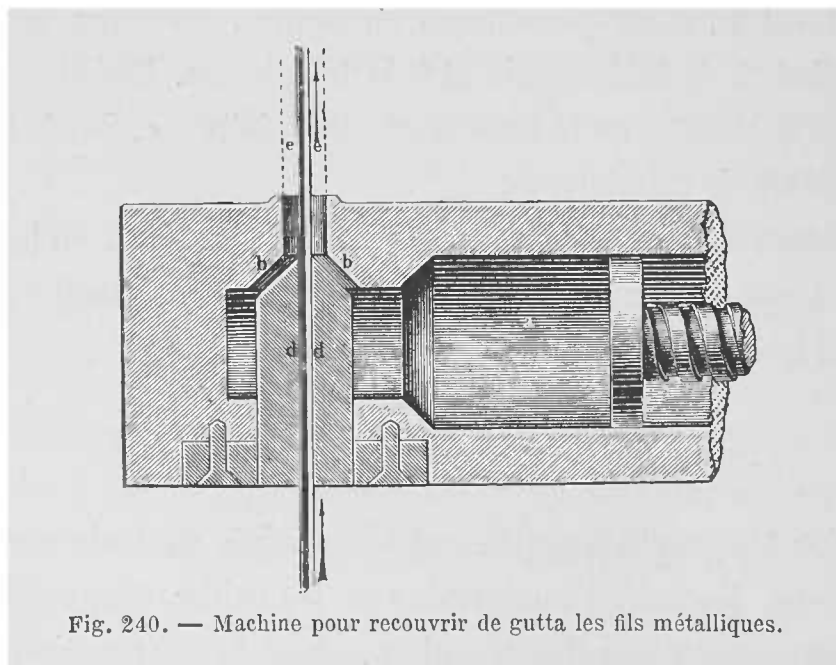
Machine pour recouvrir de gutta les fils métalliques.
